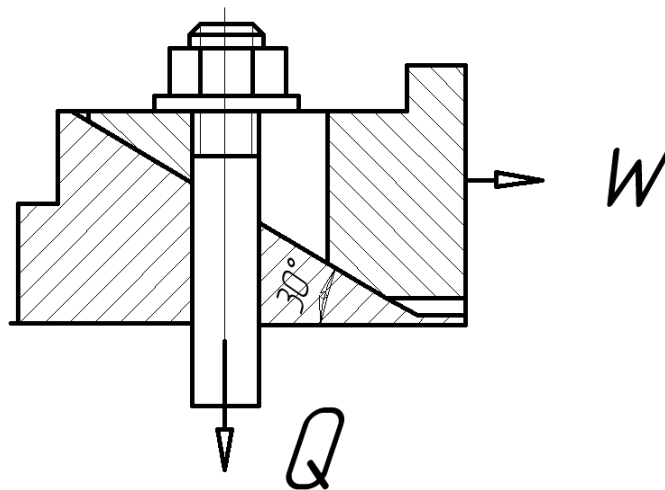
Схема клинового механізму для передавання зусилля затиску
